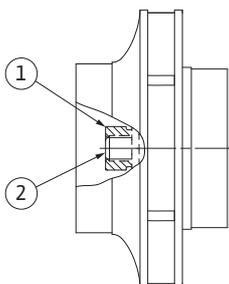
Posizione corretta del dado girante dopo il montaggio
